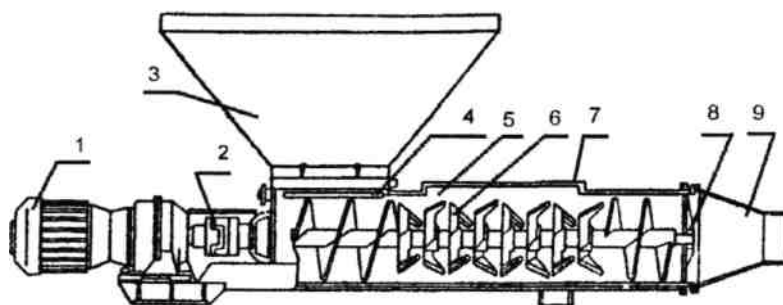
Кормосмеситель 40А: 1 — электродвигатель; 2 — муфта; 3 — загрузочный бункер; 4 — устройство для подачи воды; 5 — рабочая камера; 6 — месильные лопасти; 7 — смотровой люк; 8 — разгрузочное окно; 9 — коническая насадка
